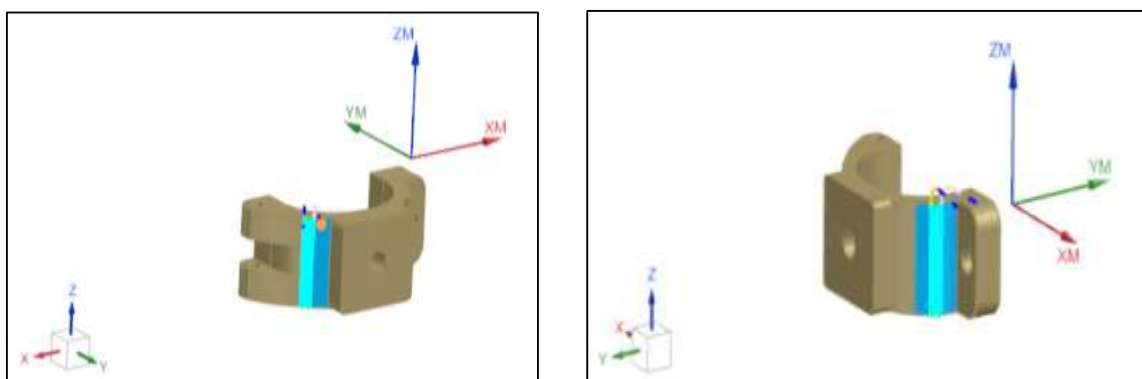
Hrubovací a dokončovací operace tvaru objímky
